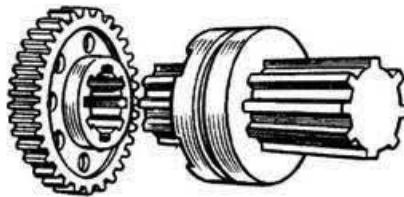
Зубчасте (шліцьове) з'єднання
